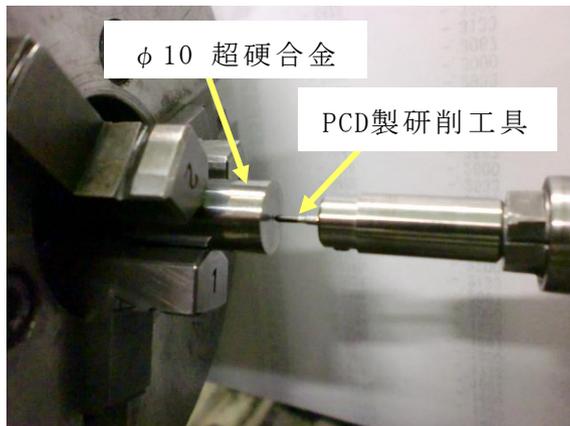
超硬合金製深絞りメス金型の加工に使用した装置の外観
